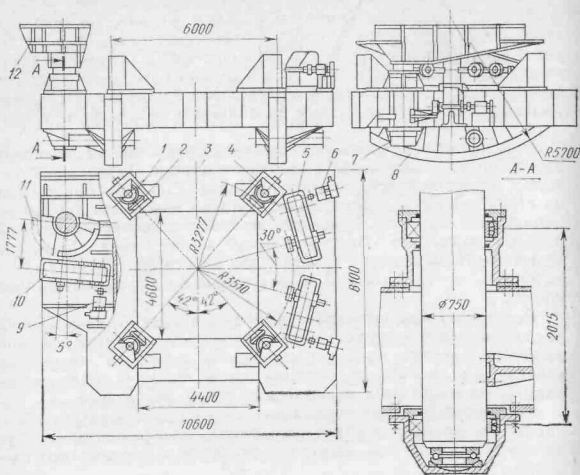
Механизм поворота корпуса и свода электрпечи:
